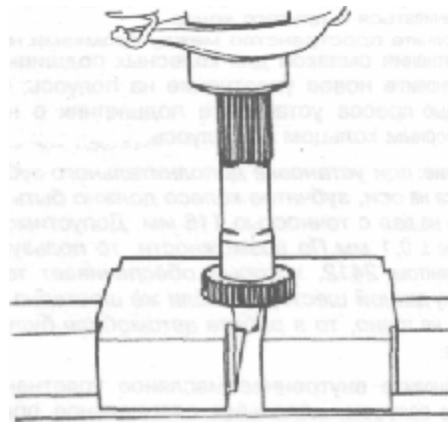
Выпрессовка зубчатого колеса. При выпressовке пользуйтесь двумя V-блоками
